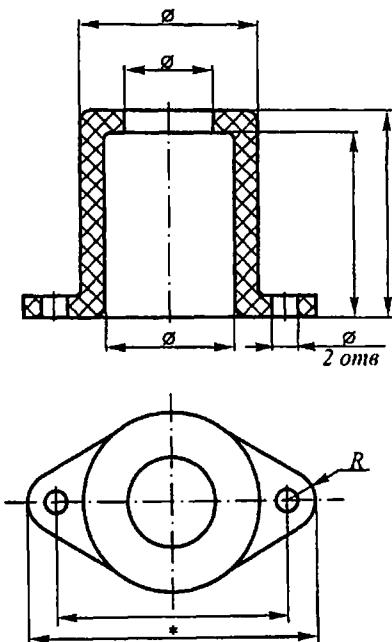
Приклад кресленика деталі з пластмаси
